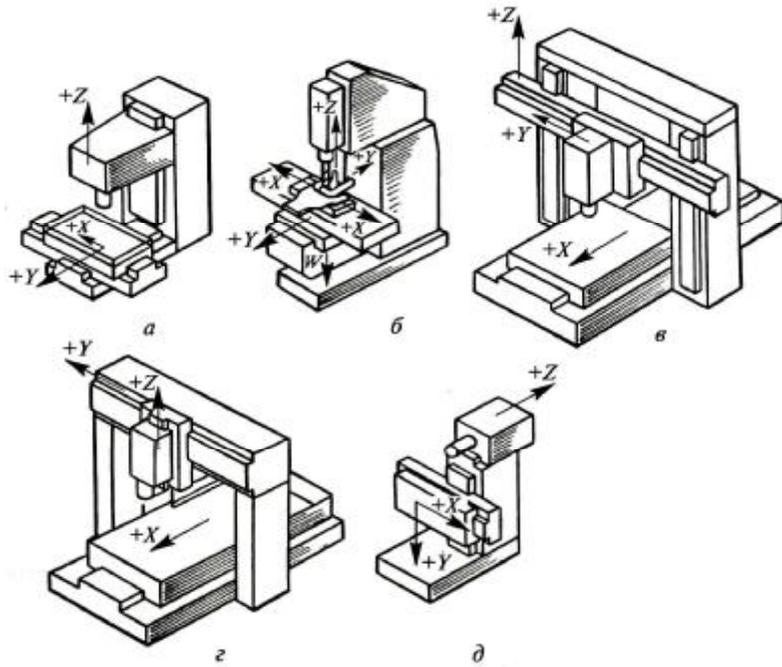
Фрезерные станки с ЧПУ (X , Y , Z , W – оси координат): *a* – вертикальный с крестовым столом; *б* – консольно-фрезерный; *в* – продольно-фрезерный; *г* – продольно-фрезерный с неподвижной поперечиной; широкоуниверсальный инструментальный
